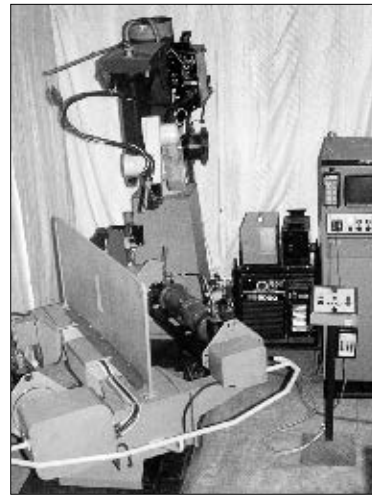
РТК дуговой сварки изделия «корпус охладителя»
